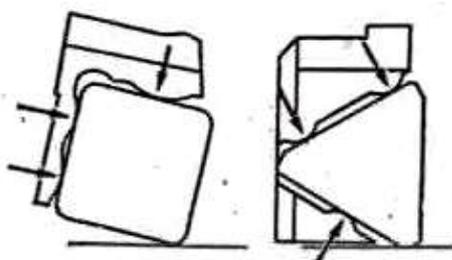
Метод установки твердосплавных пластинок на три точки по трем точкам позволяет добиться геометрически однозначной установки пластинки во фрезе.
